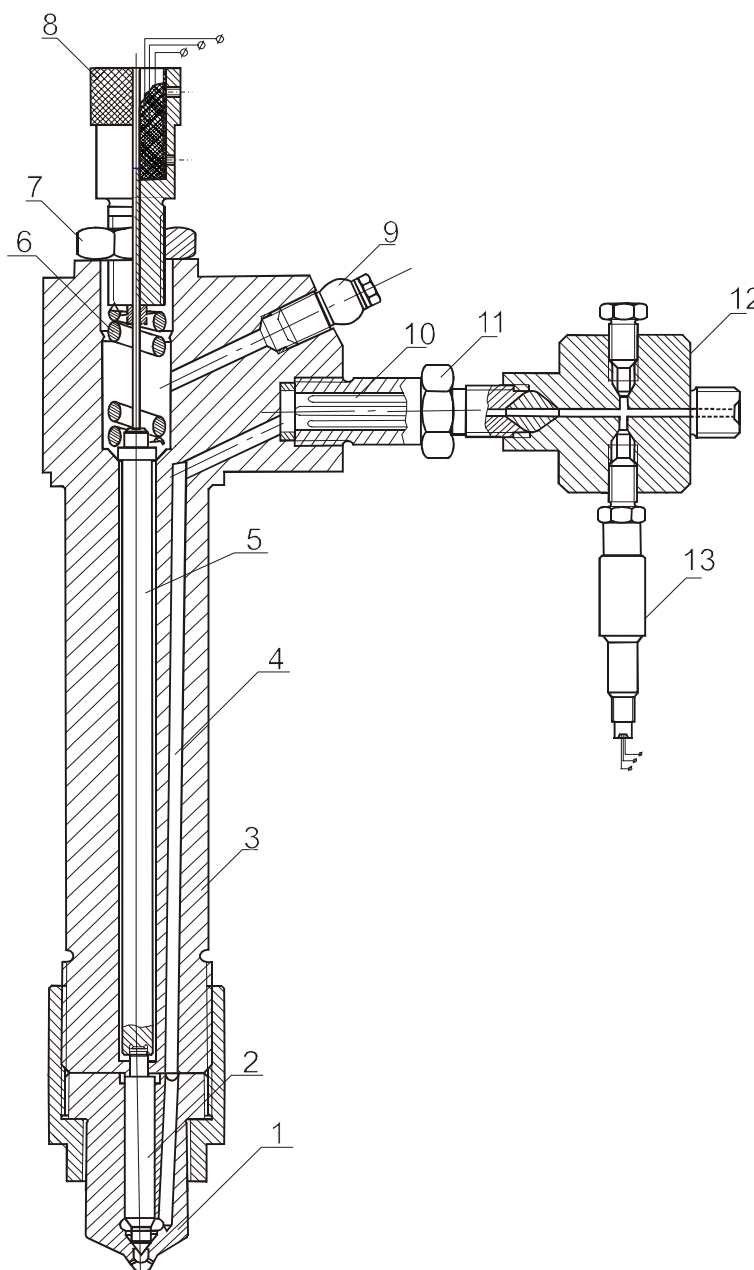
Форсунка с датчиками: 1 — сопло; 2 — игла; 3 — корпус; 4 — канал; 5 — толкатель; 6 — пружина; 7 — гайка; 8 — датчик подъема иглы; 9 — отвод; 10 — щелевой фильтр; 11 — корпус фильтра; 12 — переходник; 13 — датчик давления топлива
